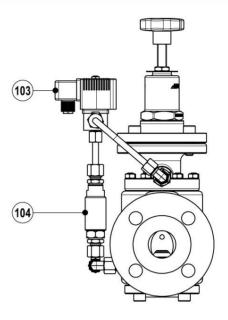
Válvula com eletroválvula para fechamento remoto
